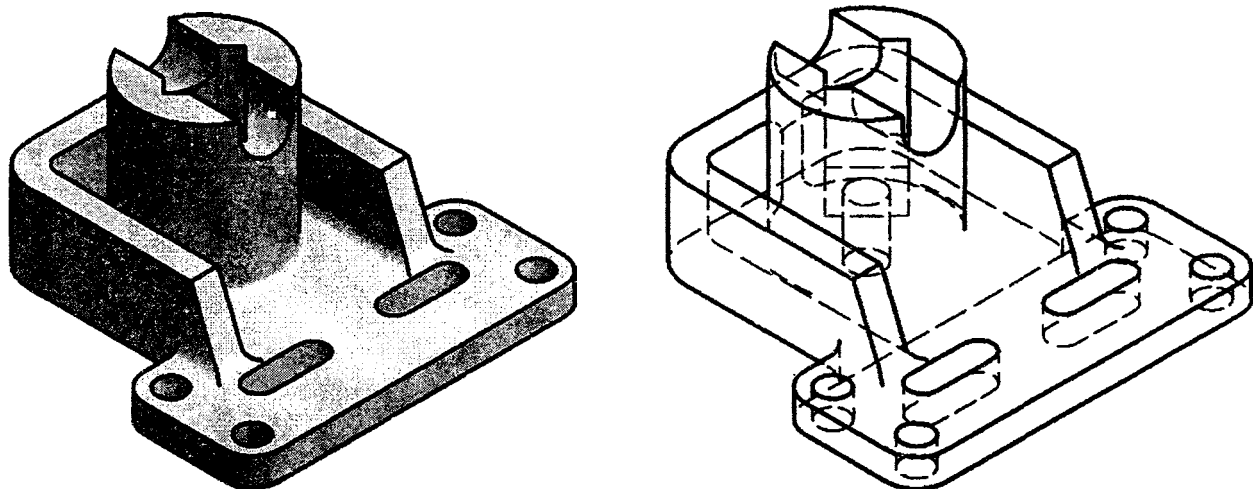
Образец детали, чертеж которой (рис. 3.12) содержит ступенчатый разрез
